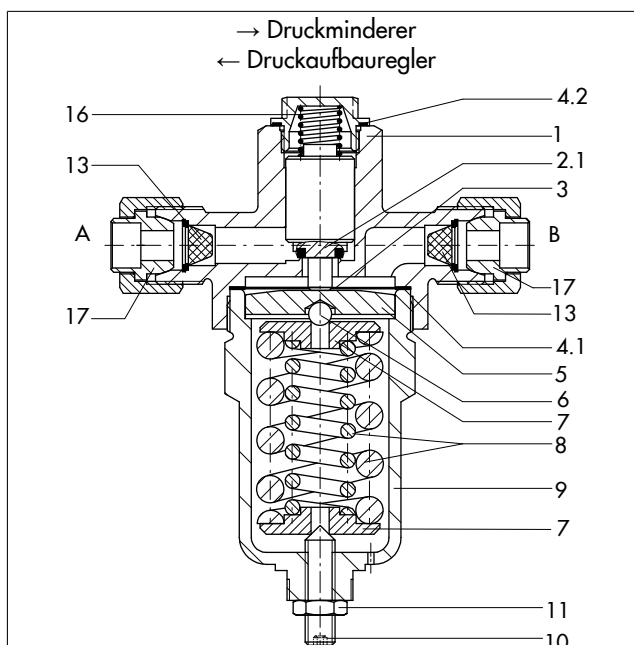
Druckaufbauregler oder Druckminderer Typ 2357-1 (PN 50)
